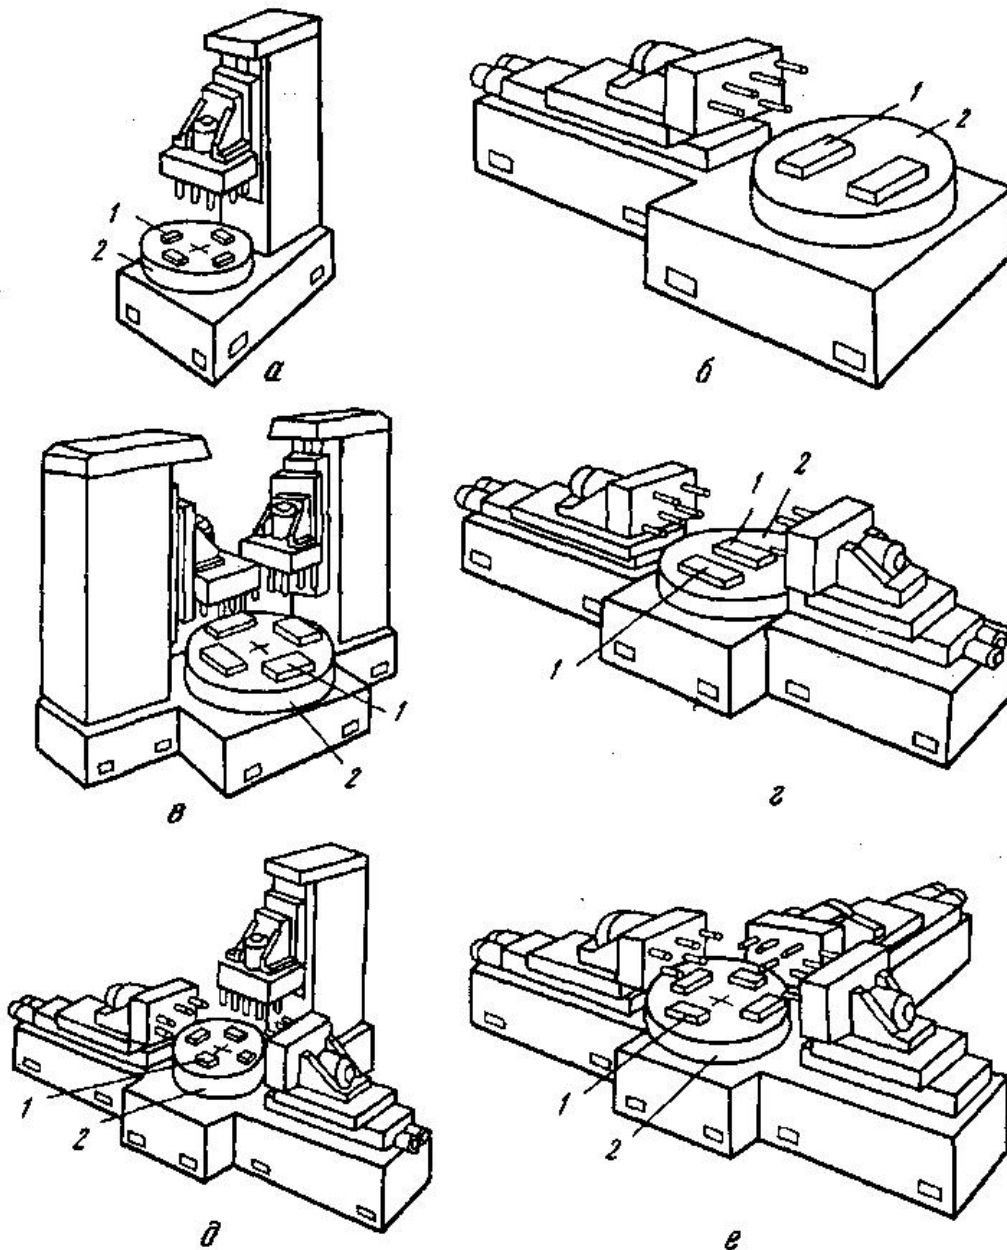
Типові компоновки агрегатних верстатів з поворотним ділильним столом
